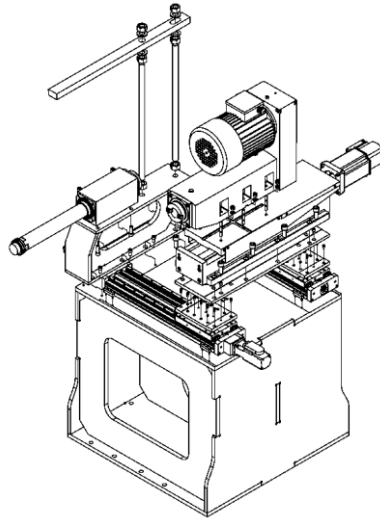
Perspetiva isométrica explodia “Assembly final CM”.
